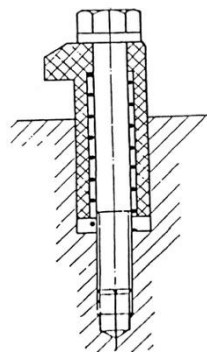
Brida de Gancho para Sujeción poco Voluminosa
